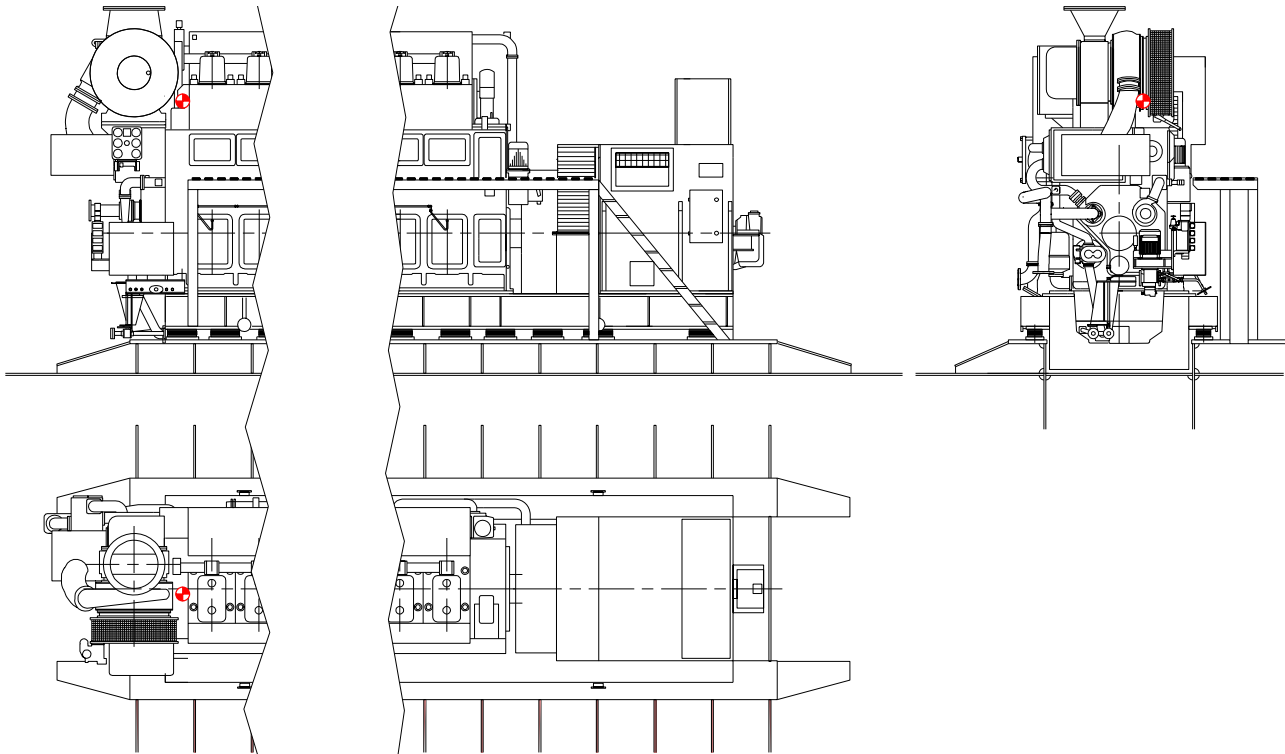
Esquema del motor auxiliar y posición de las líneas de combustible.
